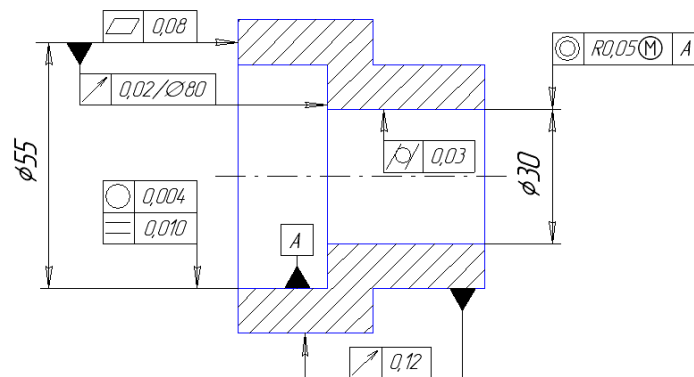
Позначення допусків форми та розташування на кресленіку
